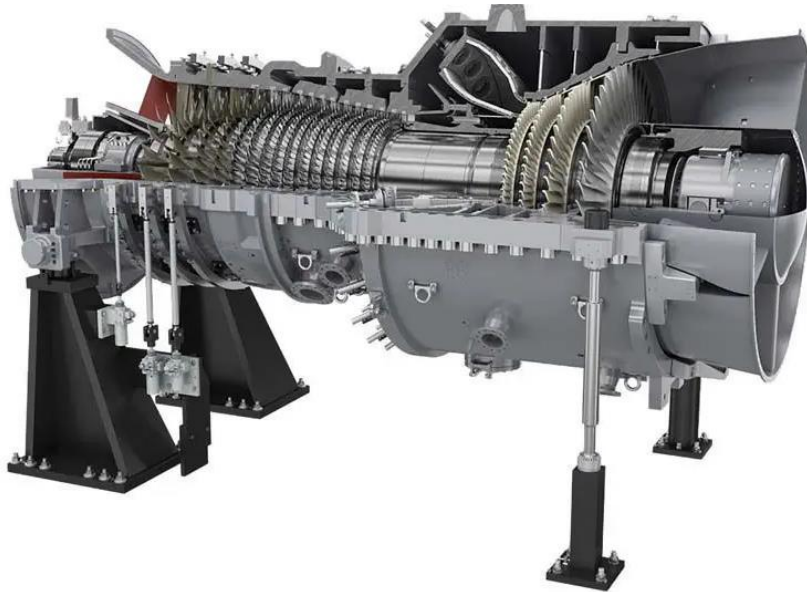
La turbine à gaz SGT5-4000F [5]
